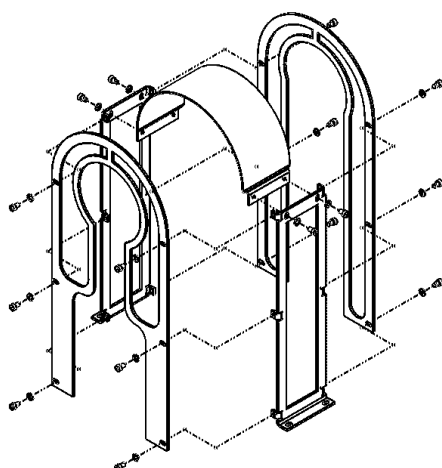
Perspetiva isométrica explodia do desenho de conjunto “Assembly proteção correia CF”.
